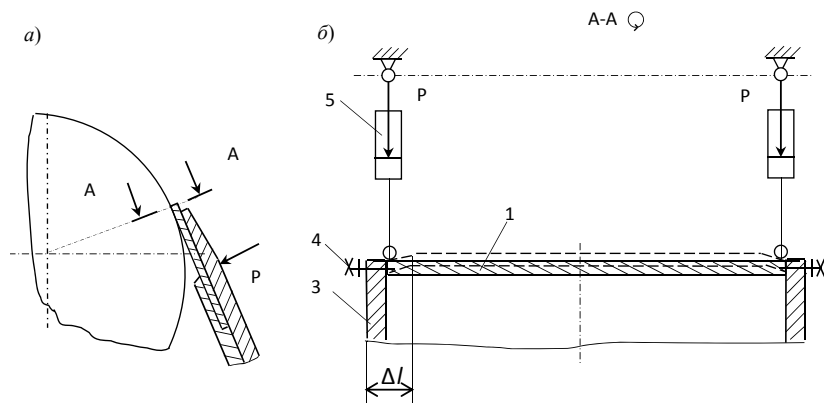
Схема взаимодействия крепирующего шабера с поверхностью Янки-цилиндра: а – вид с лицевой стороны; б – разрез по А-А
